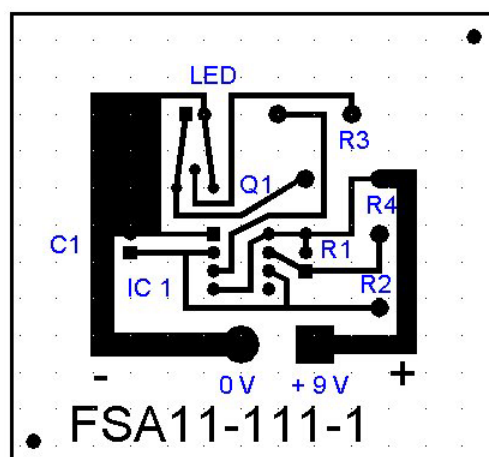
Exemple de dessin transféré à la machine-outil gravant la plaque
